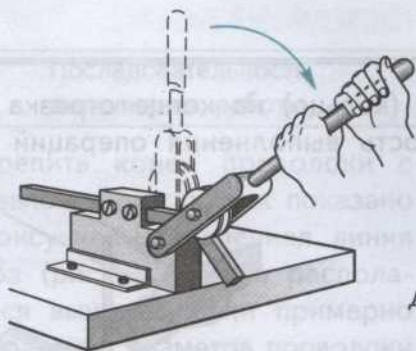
Гибочное приспособление для изготовления рамки ножовочного станка
